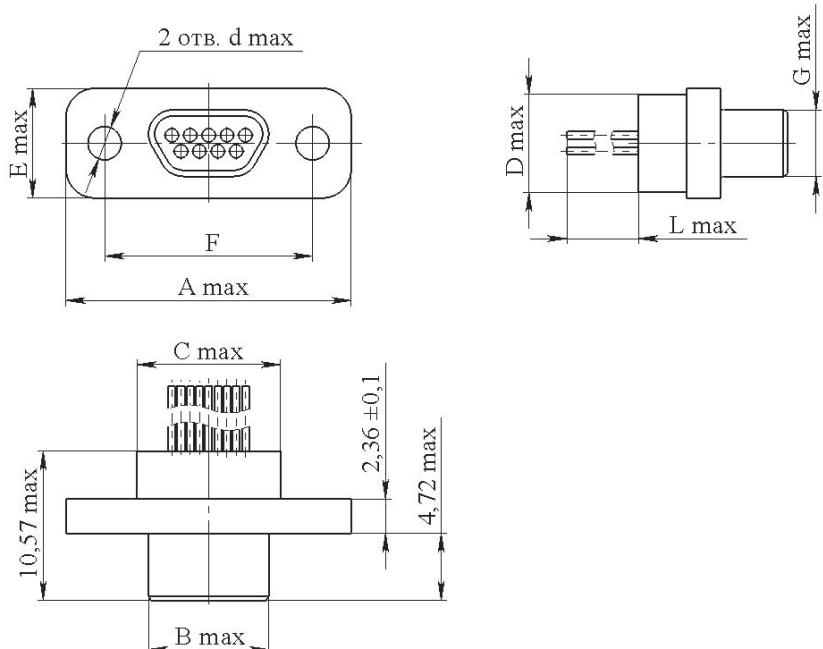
Соединитель СП397-1...Ш213(4)
